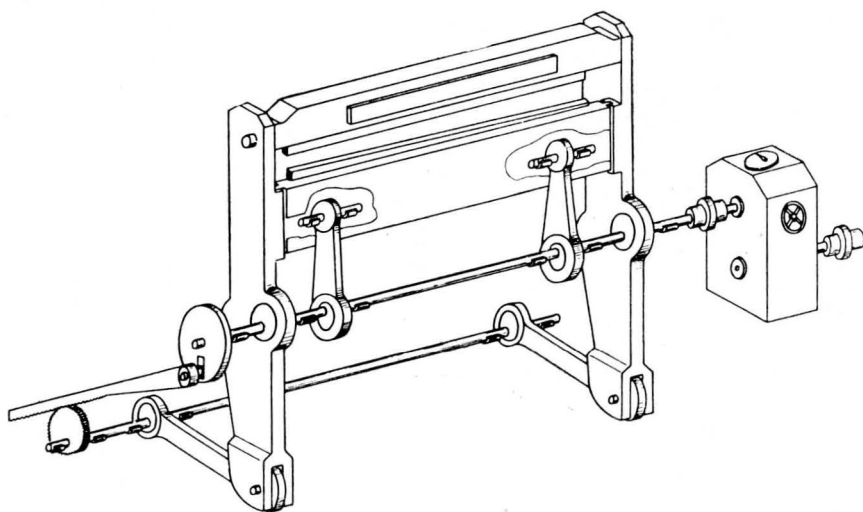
Princípio de uma tesoura automática para sub-dividir fitas; construção antiga.
